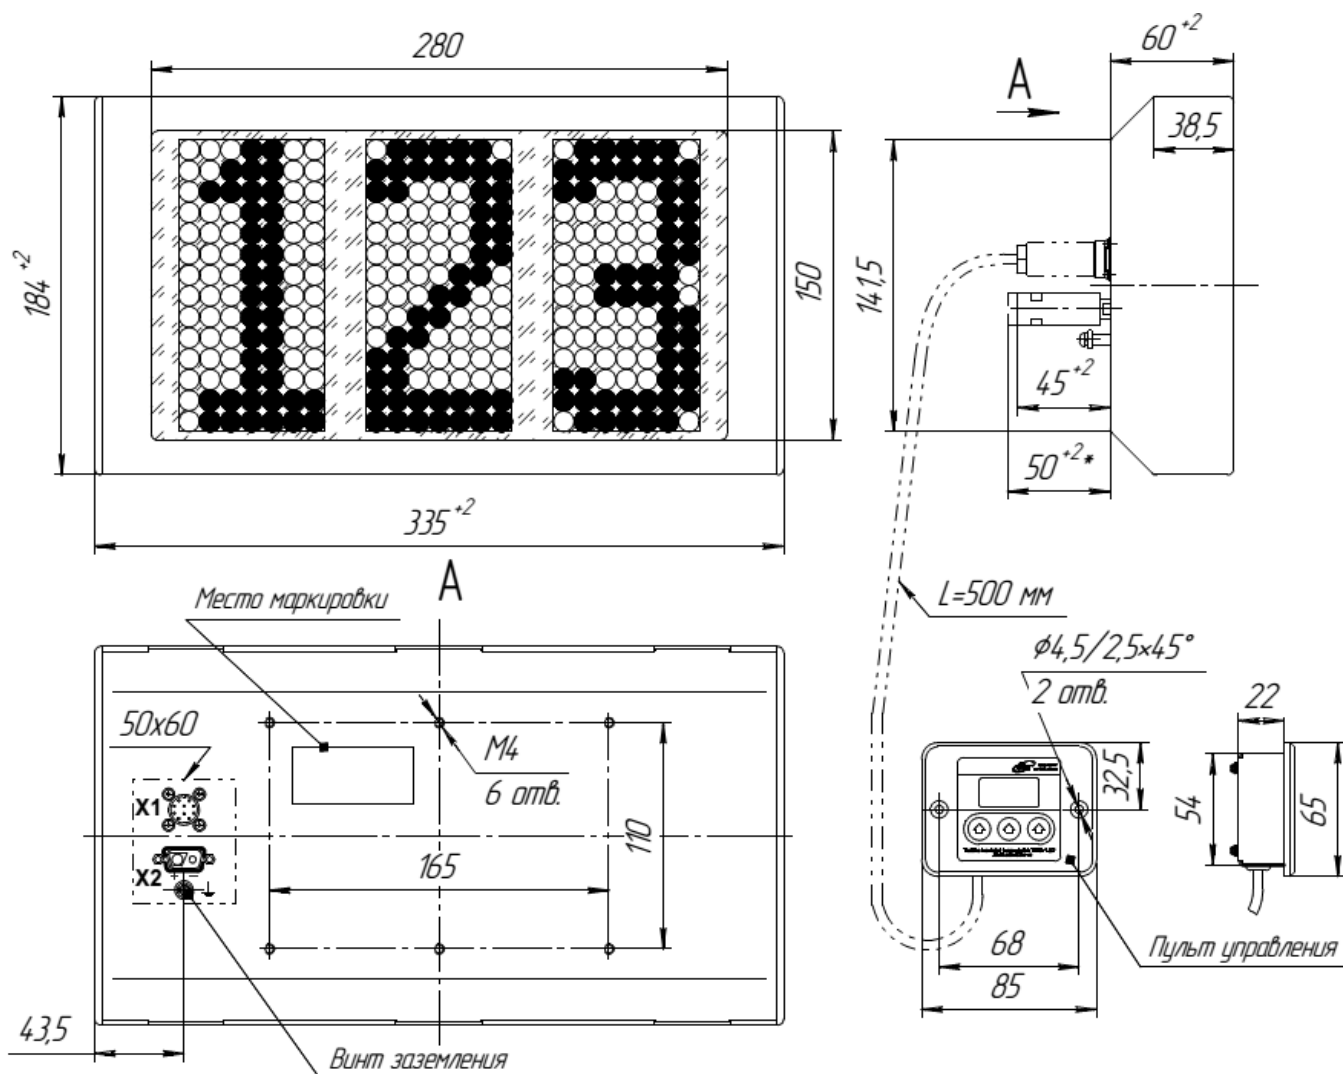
Габаритные и присоединительные размеры ТНМ-1.02
